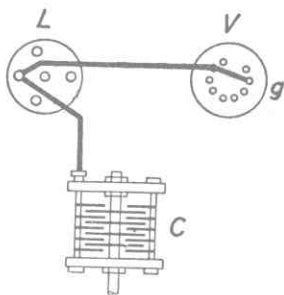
Disposizione sbagliata, collegamenti troppo lunghi.
